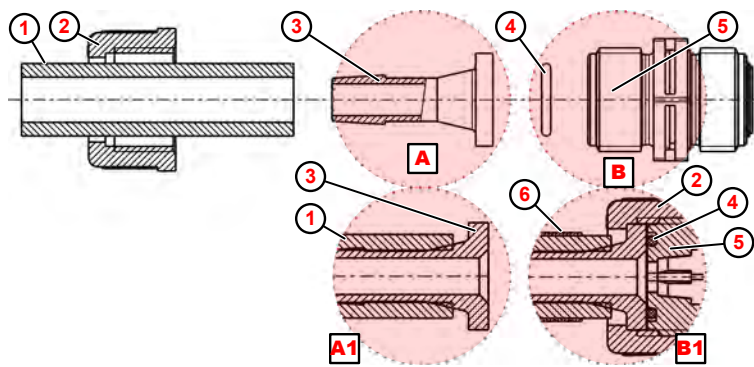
Raccord de conduit et flexible avec embout et collier de serrage
